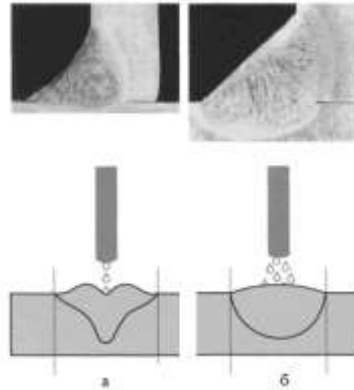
Формування шва при зварюванні (наплавленні): а – суцільним дротом; б – порошковим дротом
